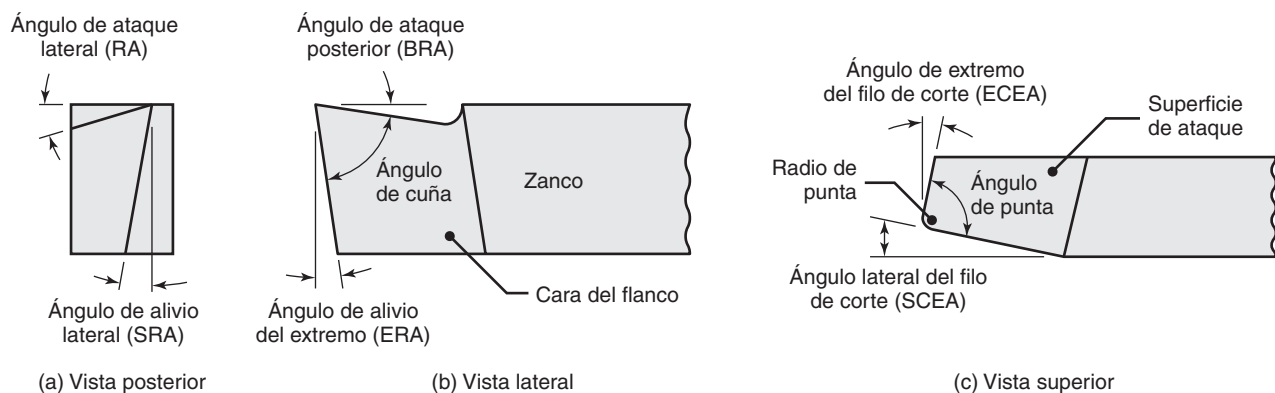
Designaciones de herramienta de corte derecho. El término *derecho* se refiere al avance de las herramientas de derecha a izquierda, como se muestra en la figura 23.3.
